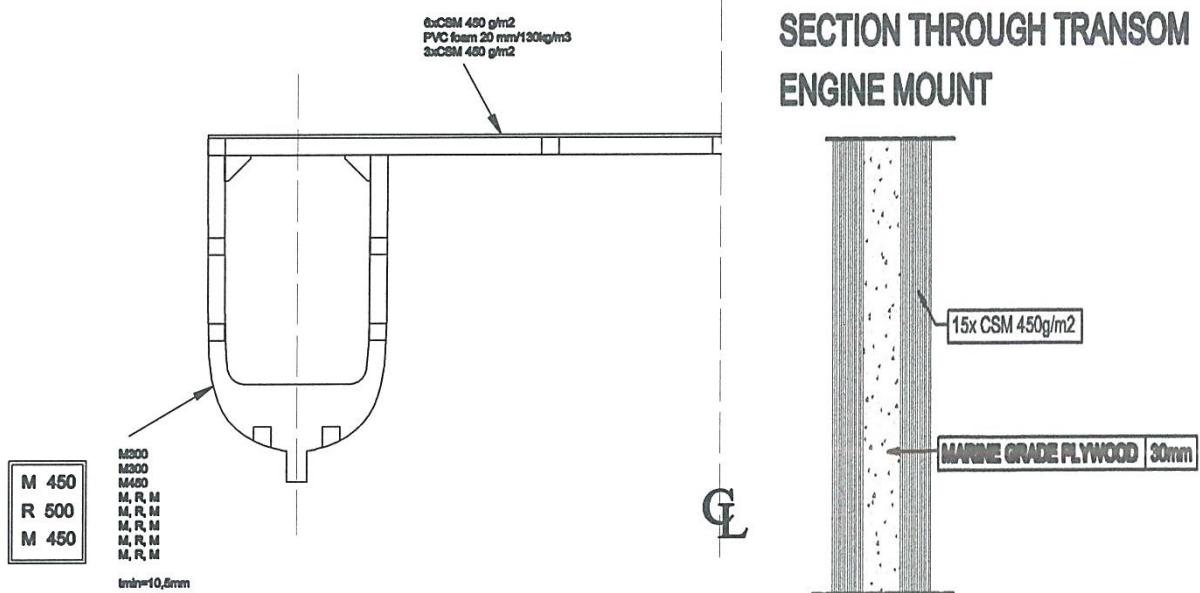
Laminate plan (palbna ukrepa).<sup>101</sup>
